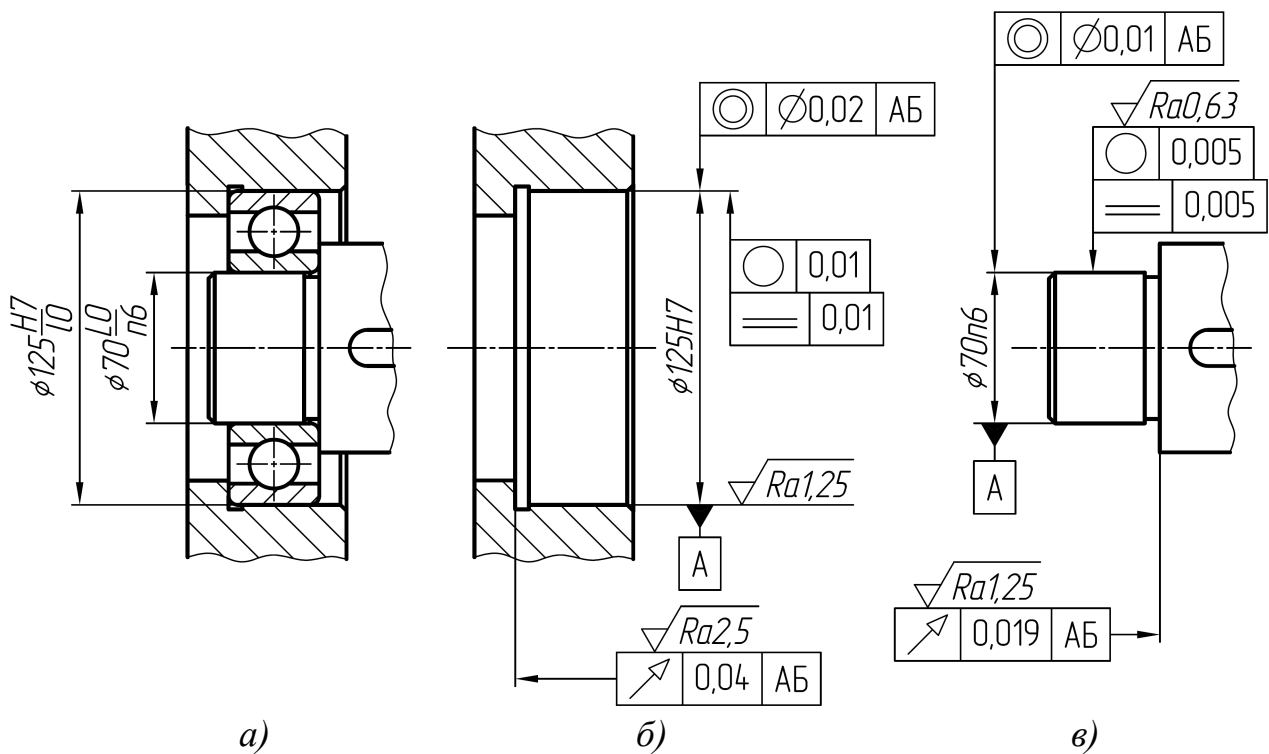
Ескізи: а) з'єднання; б) корпус; в) вал
